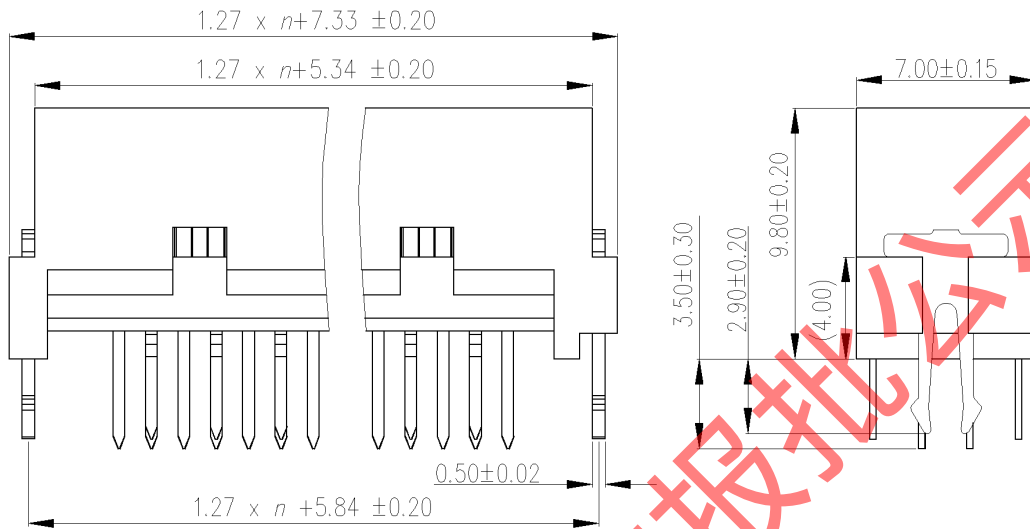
D 类型插头 180 度穿孔焊接式外形尺寸
